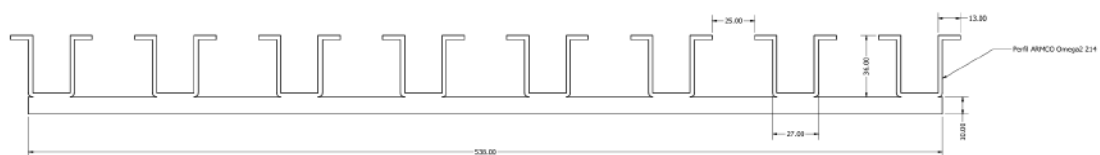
Vista frontal de la placa base (perfiles omega soldados a la placa principal).
